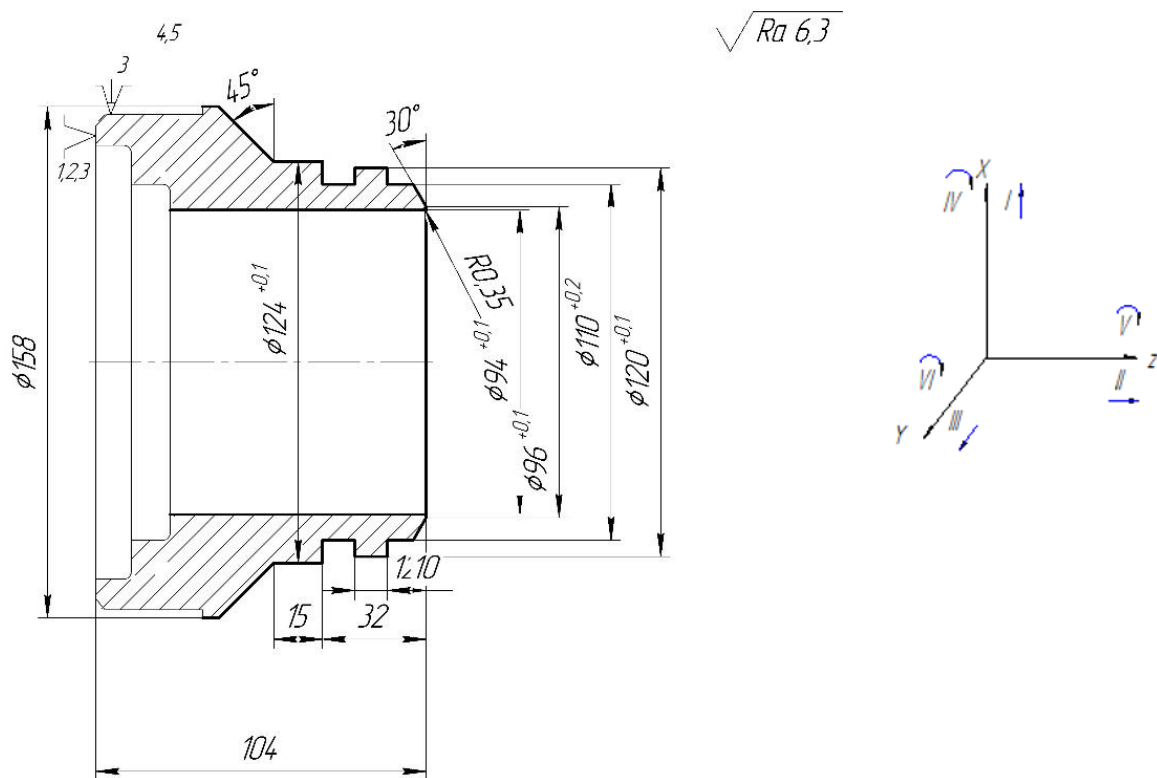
Схема базування заготовки на операції комплексній з ЧПК 015, позиція 1
